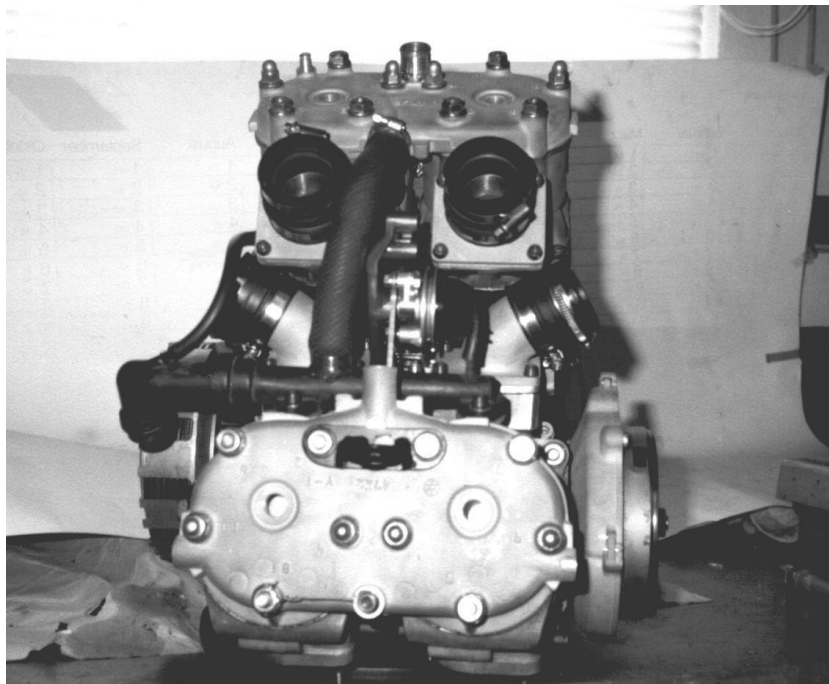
Fried Motor mit selbst gefrästen Ansaugstutzen für 34'er RGV Vergaser
